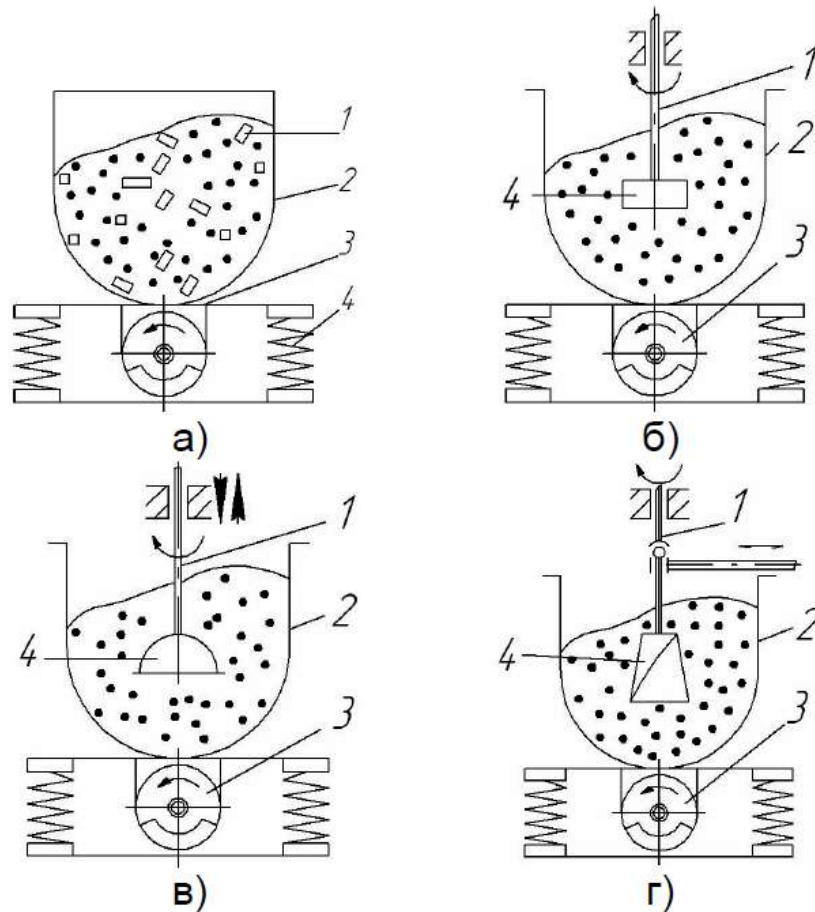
Схеми вібраційної обробки деталей : а - обробка деталей «внавал»; б, в, г - шпиндельна віброобробка
